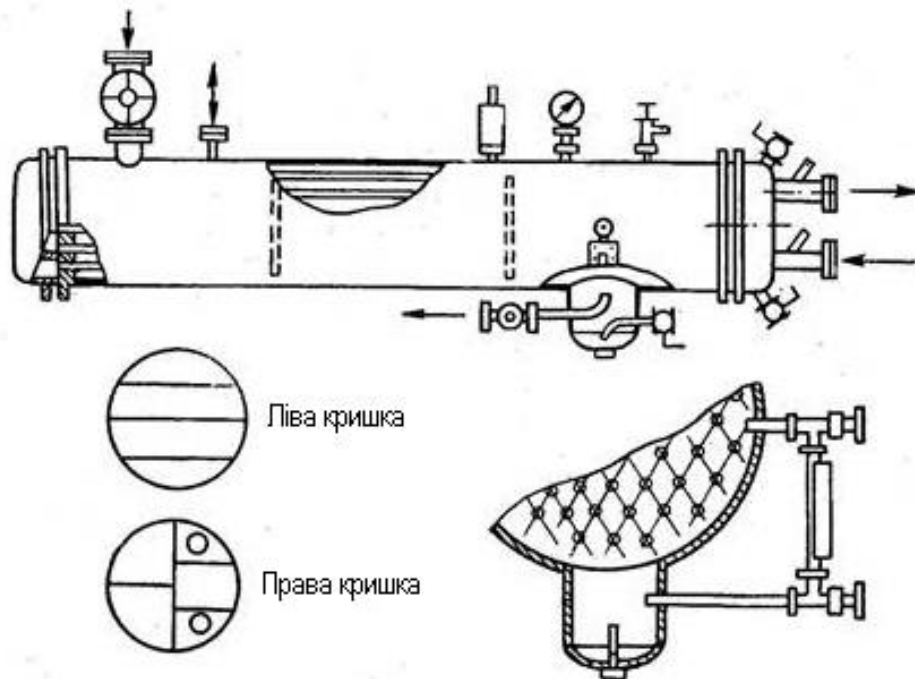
Горизонтальний кожухотрубний конденсатор
